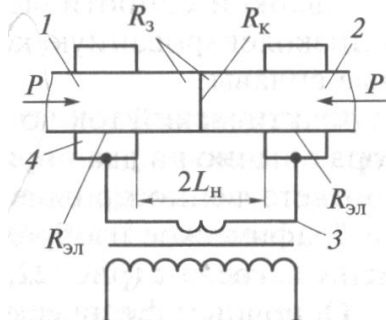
Схема стыковой контактной сварки: 1, 2 — свариваемые заготовки; 3 — трансформатор; 4 — медная подкладка; P — усилие прижима электродов; $R_з$, $R_к$, $R_{эл}$ — сопротивление соответственно заготовки, сварочного контакта и электродов
